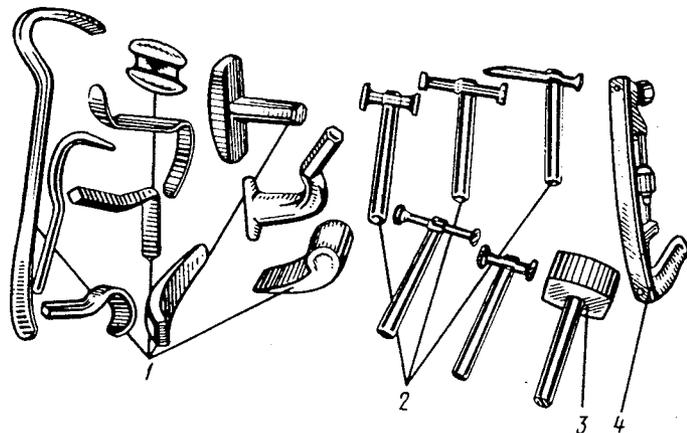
Werkzeugsatz zum Richten des Aufbaus:
